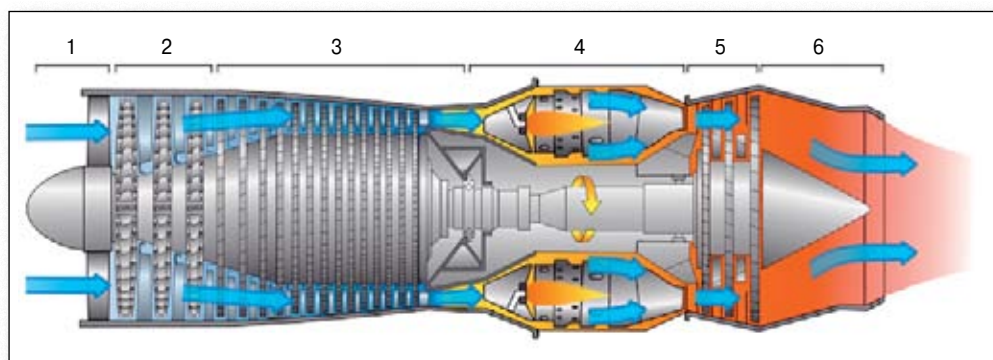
Схема турбореактивного двигателя: 1 — воздухозаборник; 2 — компрессор низкого давления; 3 — компрессор высокого давления; 4 — камера сгорания; 5 — турбина; 6 — сопло.
